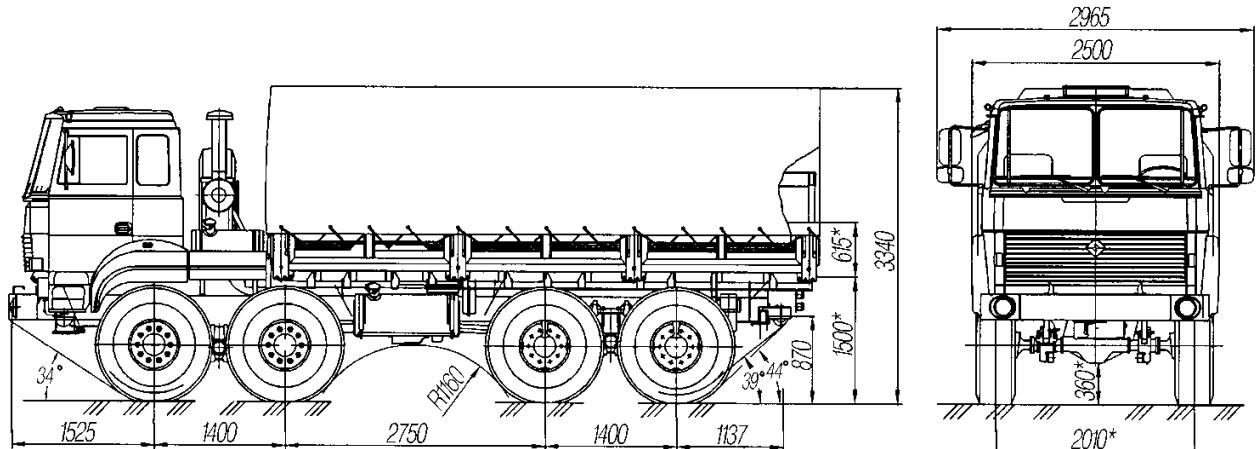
Габаритные размеры автомобиля Урал-532301-70
